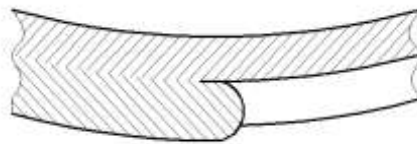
Загальний вигляд натікання металу в зоні початку зварювання
